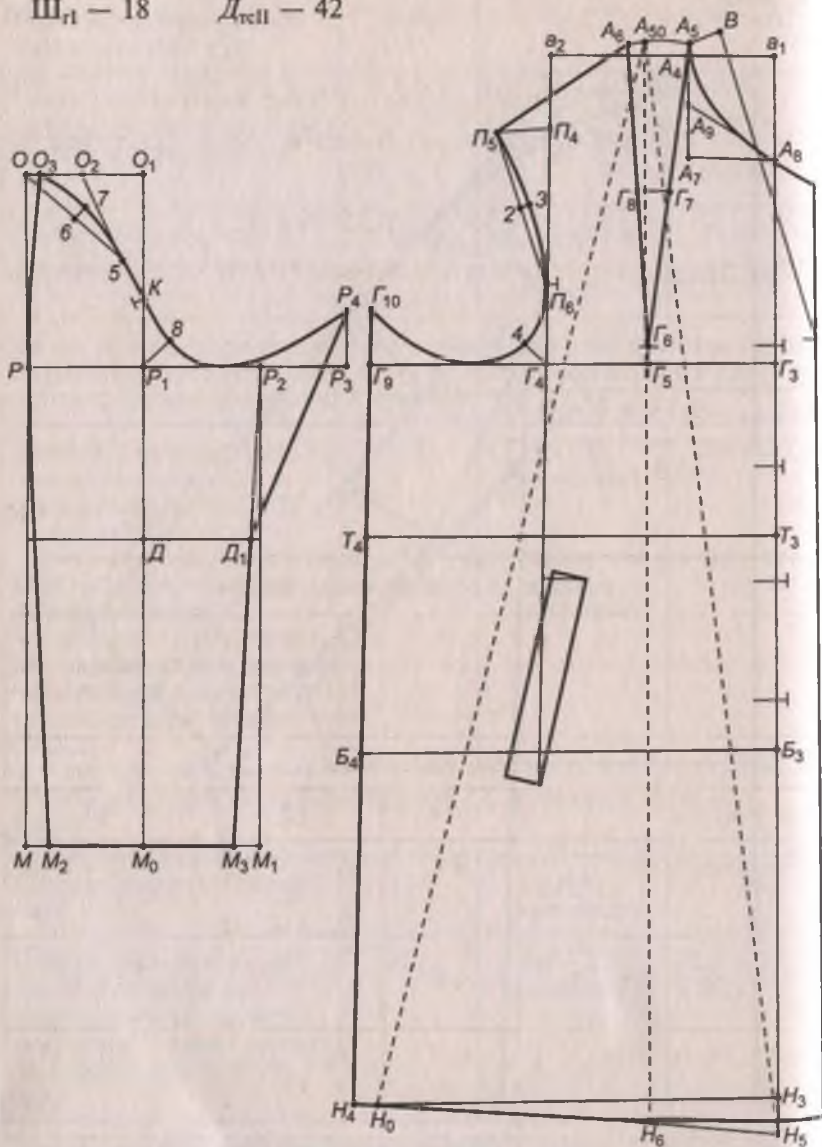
Чертеж конструкции женского пальто (полочка) с рукавами комбинированного покроя
